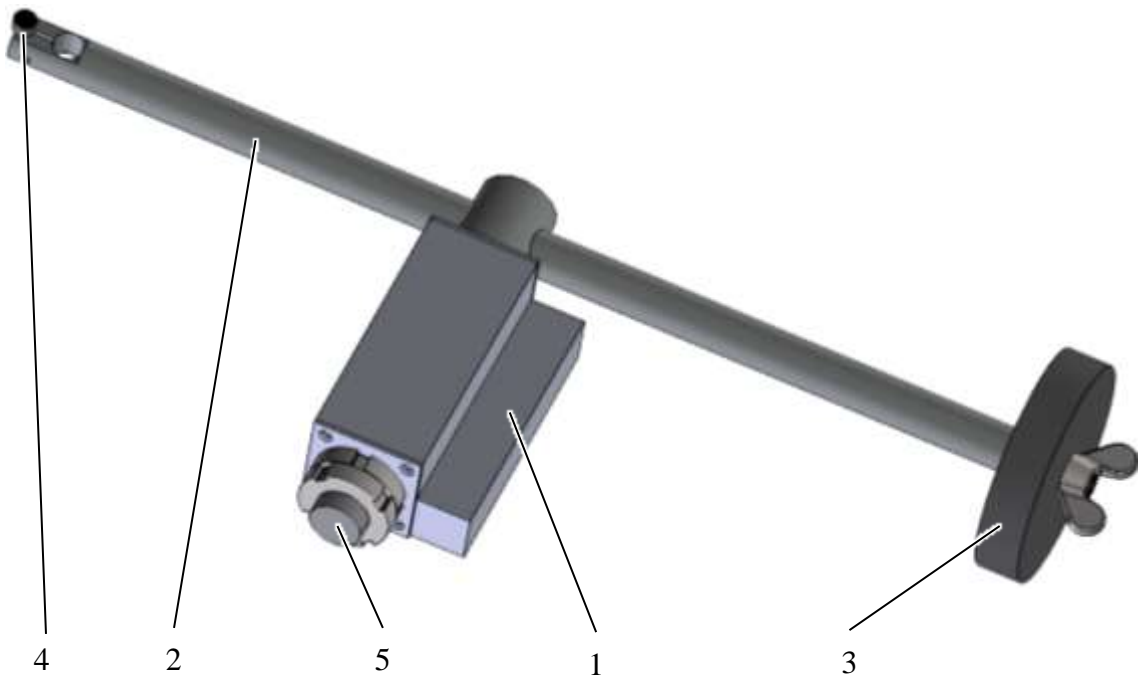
Приспособление для алмазного выглаживания: 1 – корпус; 2 – балка; 3 – груз; 4 – алмазный индентор; 5 – ось
